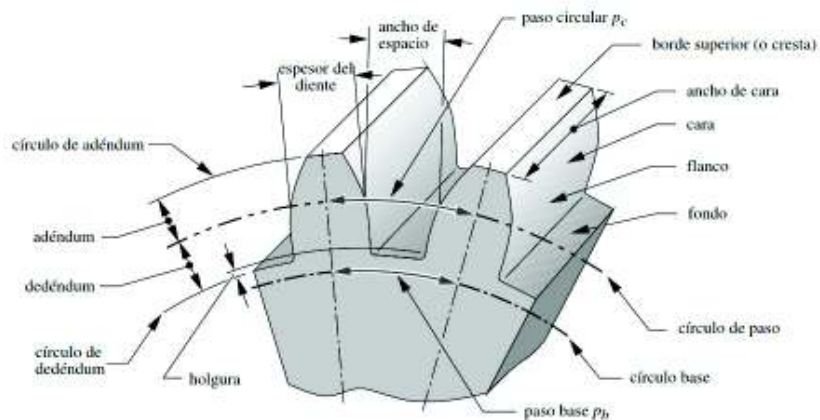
Nomenclatura de un diente de engranaje rueda motriz.
